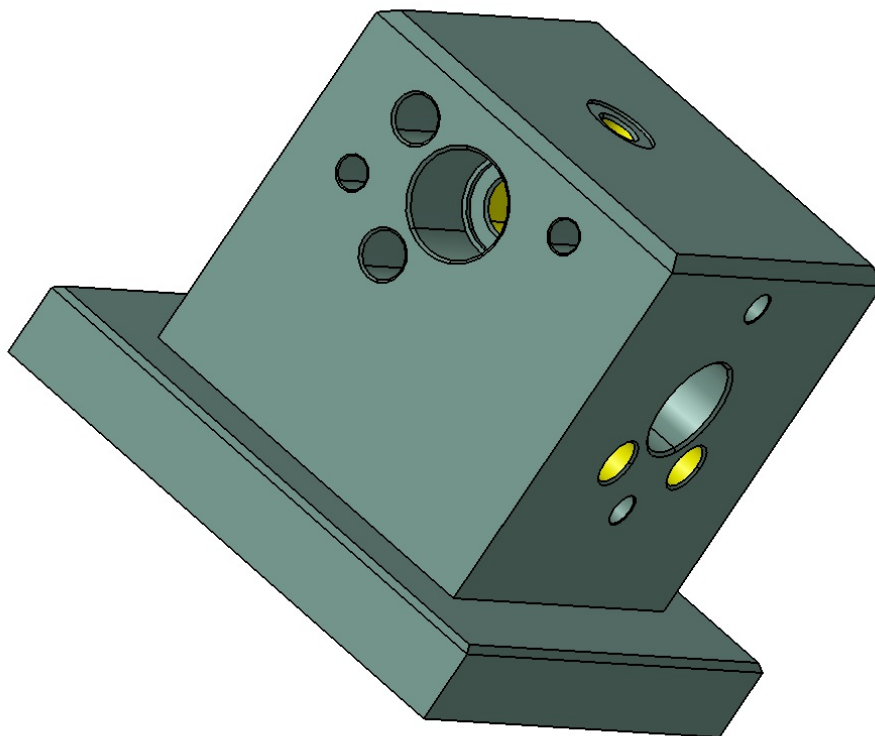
Varianta A – přípravek s ustavenými obrobky
